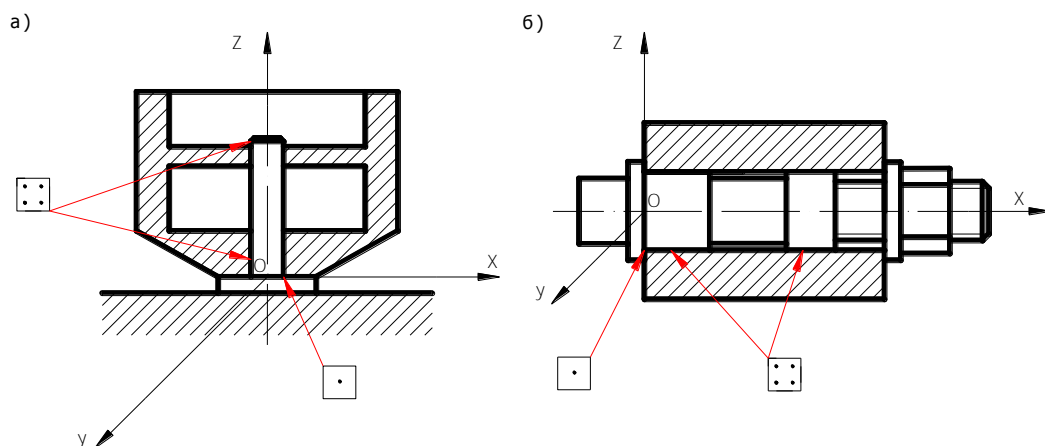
Схемы установки детали на высокий цилиндрический палец (а) и цилиндрическую оправку (б).
